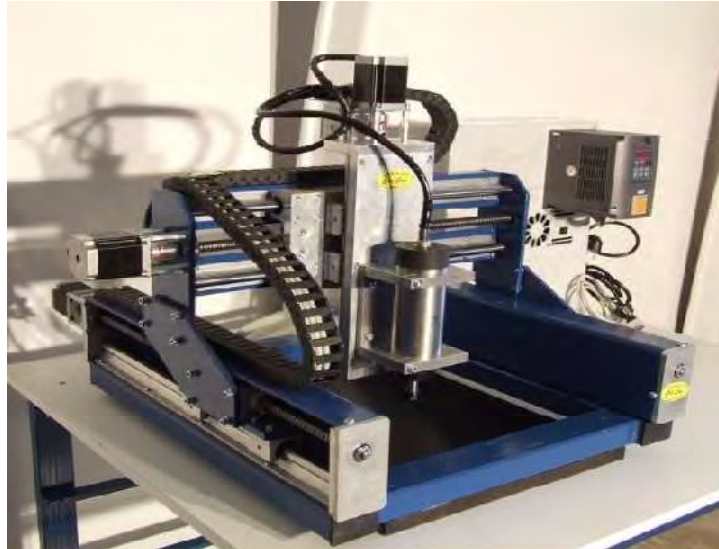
CNC-фрезерний комплекс Komras H-400 HF [4].
